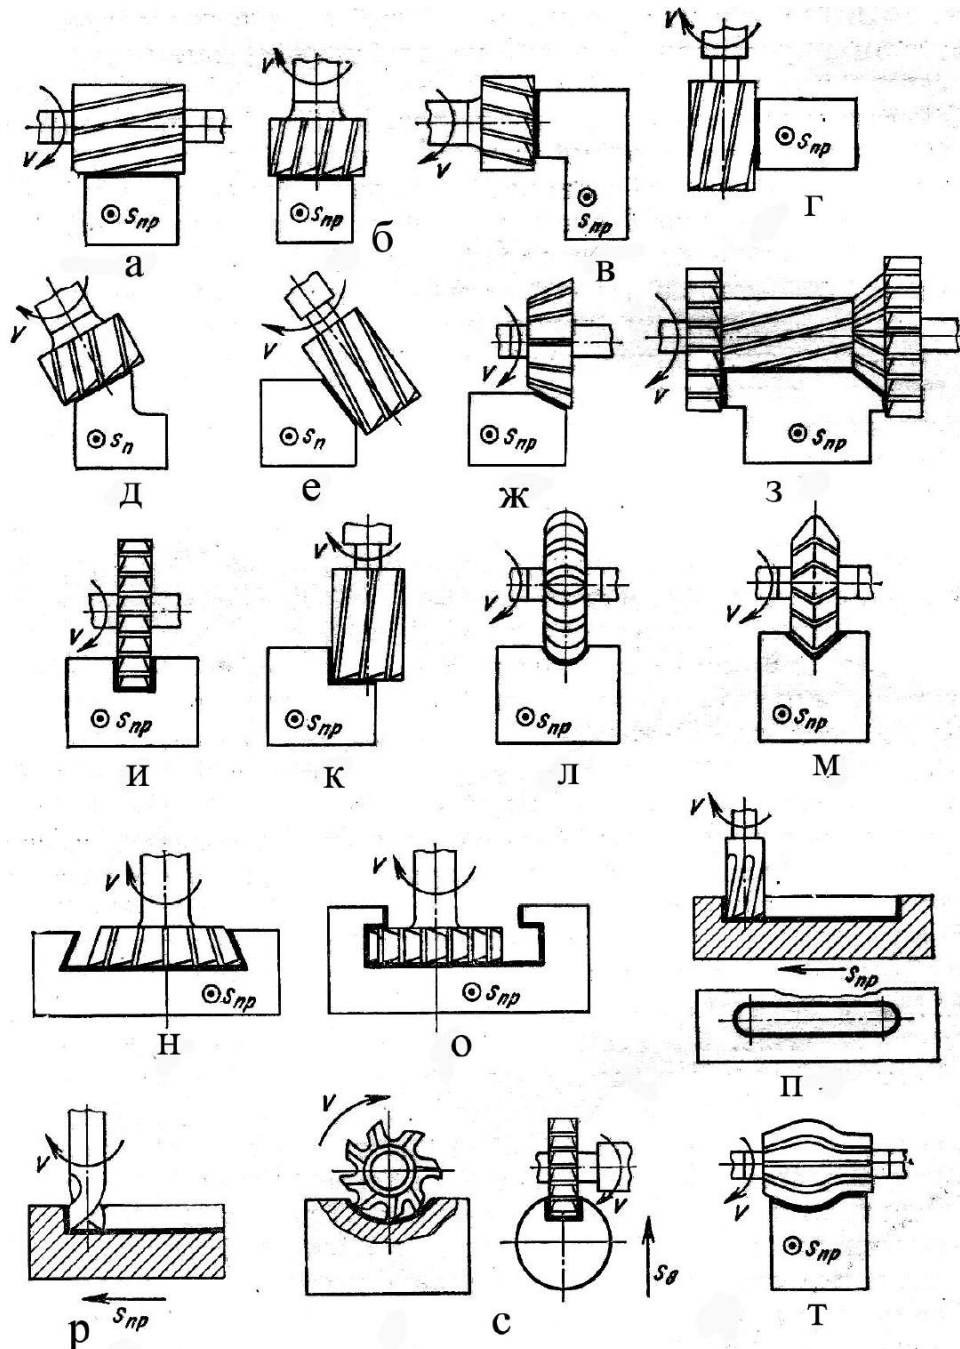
Схема обробки поверхонь заготовки на горизонтальних і вертикально-фрезерних верстатах
